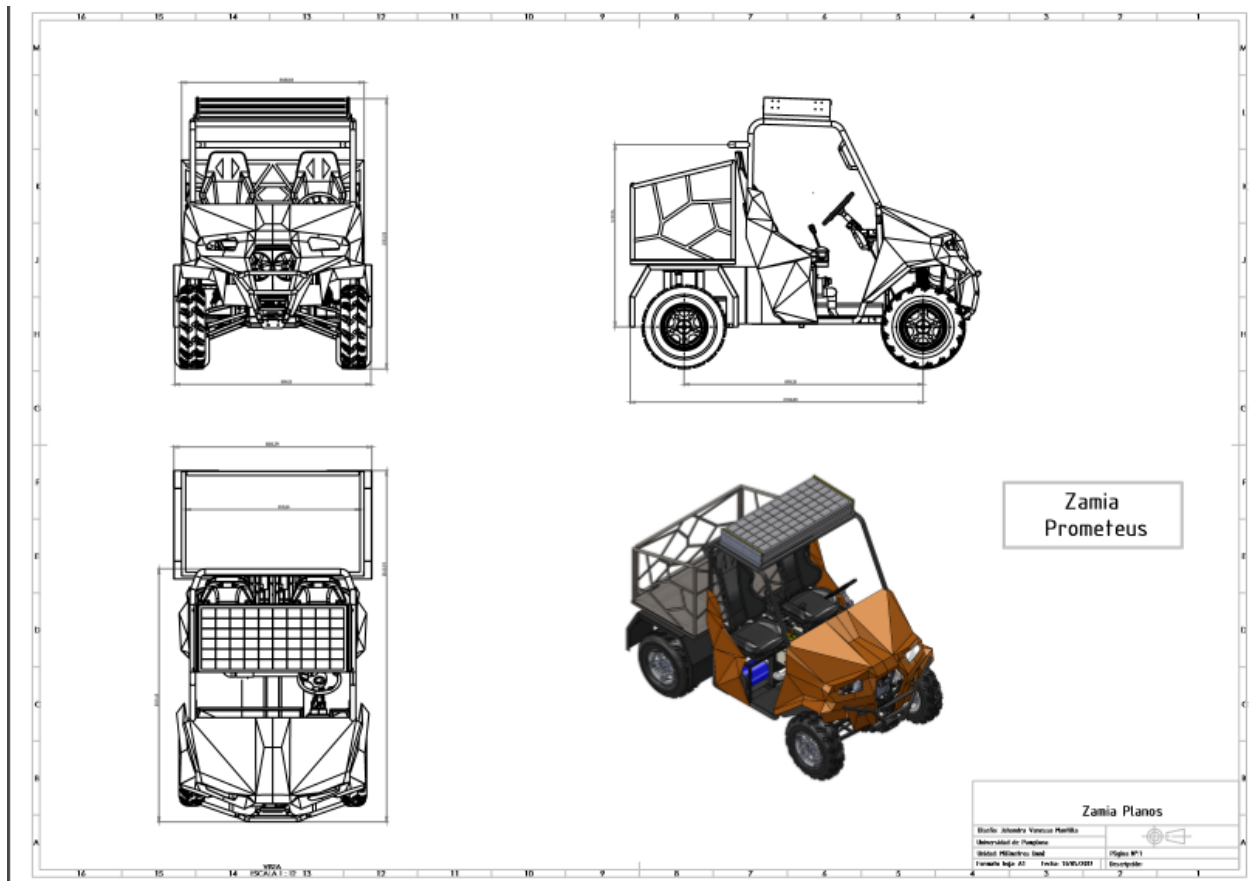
Plano técnico general del vehículo. Elaborado por Johandra Mantilla.
